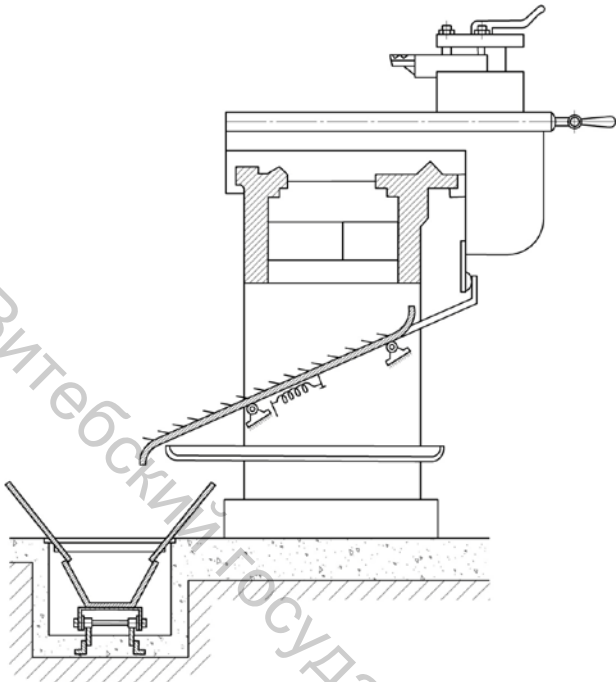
Схема устройства скребкового типа для уборки стружки из рабочей зоны станка
